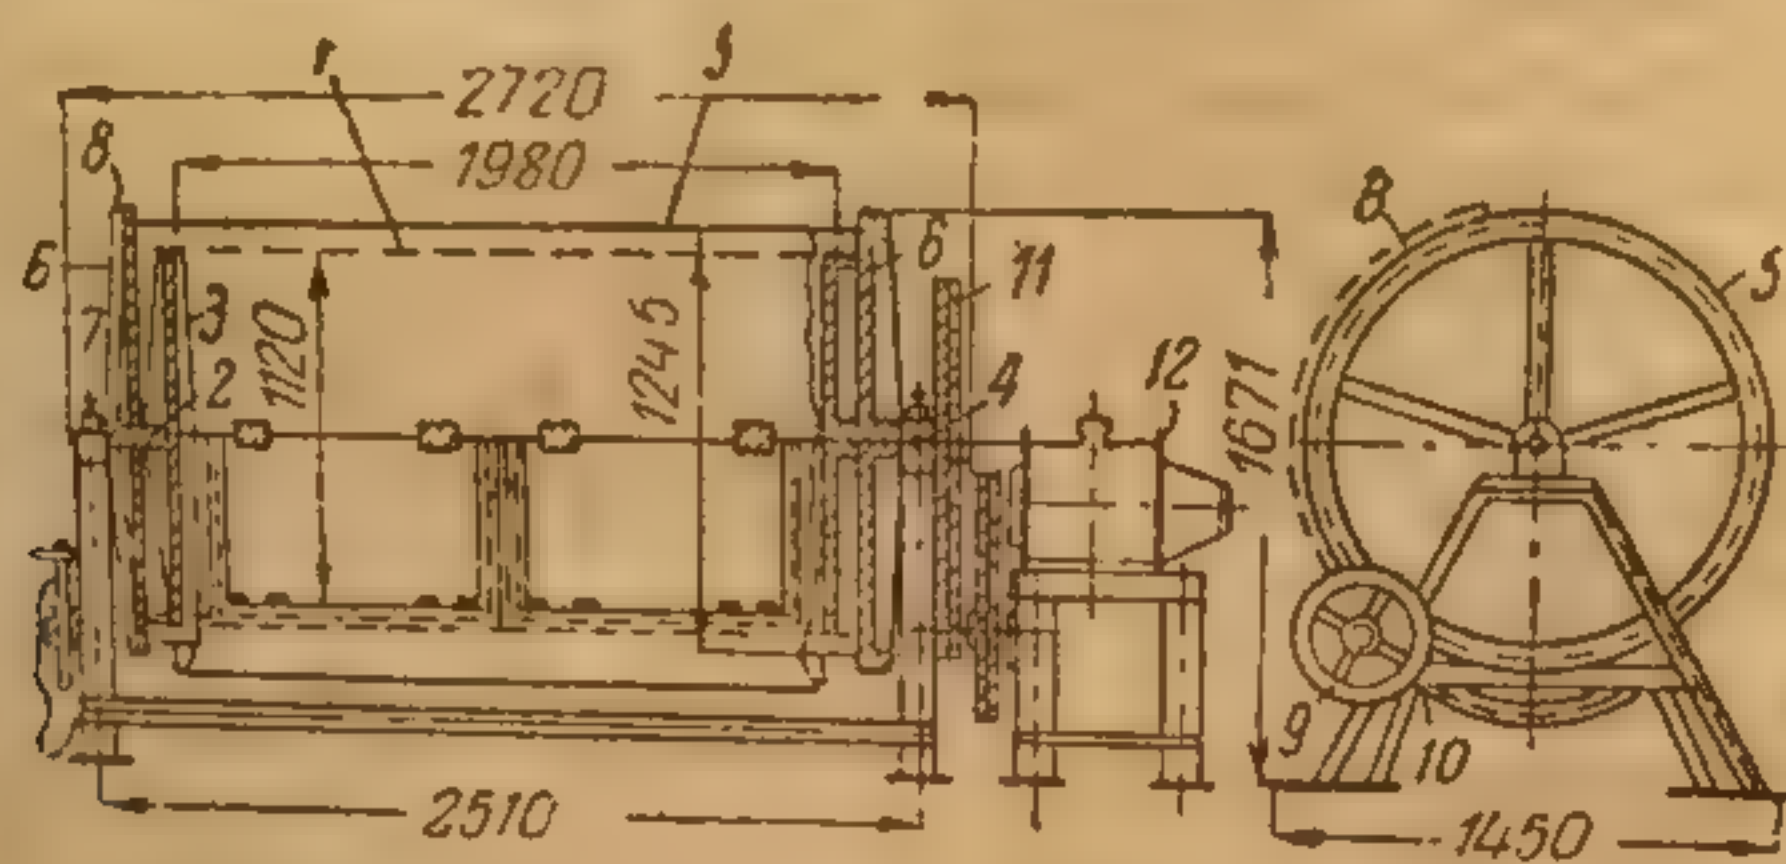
Горизонтальный моечный барабан с перфорированными поверхностями для чистки рубцов:
